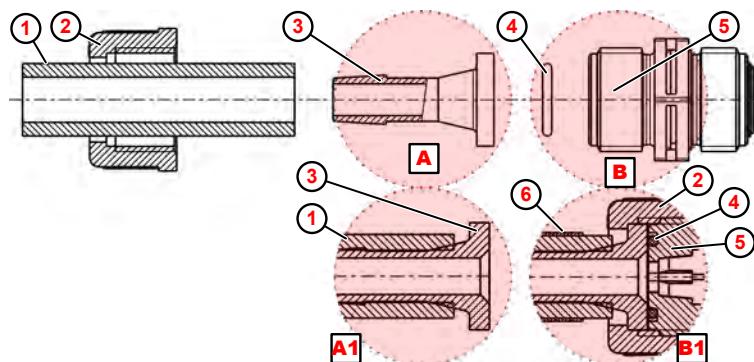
Raccord de conduit et flexible avec embout et collier de serrage
